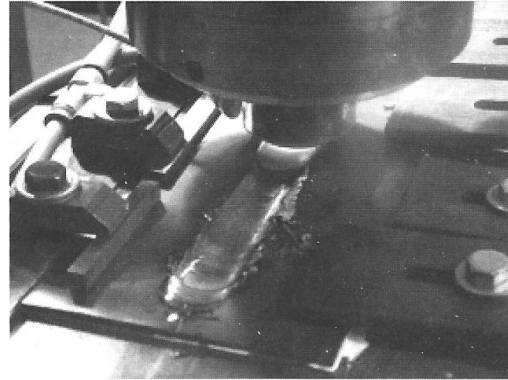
Equipo de soldadura en fase sólida de aceros por Fricción - Agitación (Friction Stir Welding) desarrollado recientemente en la Argentina empleando una herramienta de cerámica avanzada.
